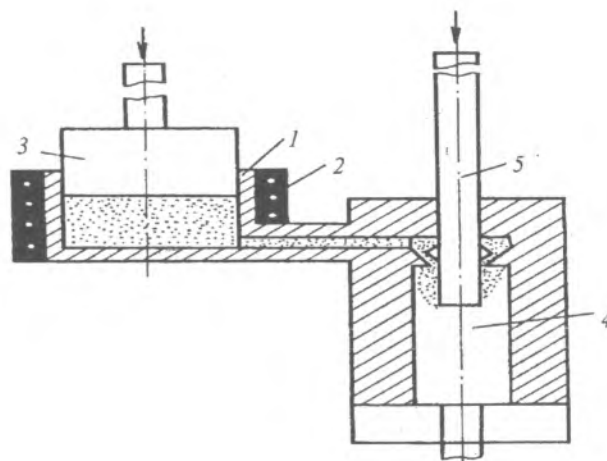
Схема экспериментальной прессформы с перемещающимся цилиндрическим знаком: 1 – загрузочная камера; 2 – нагреватель; 3 – пуансон; 4 – оформляющая полость; 5 – цилиндрический перемещающийся знак
